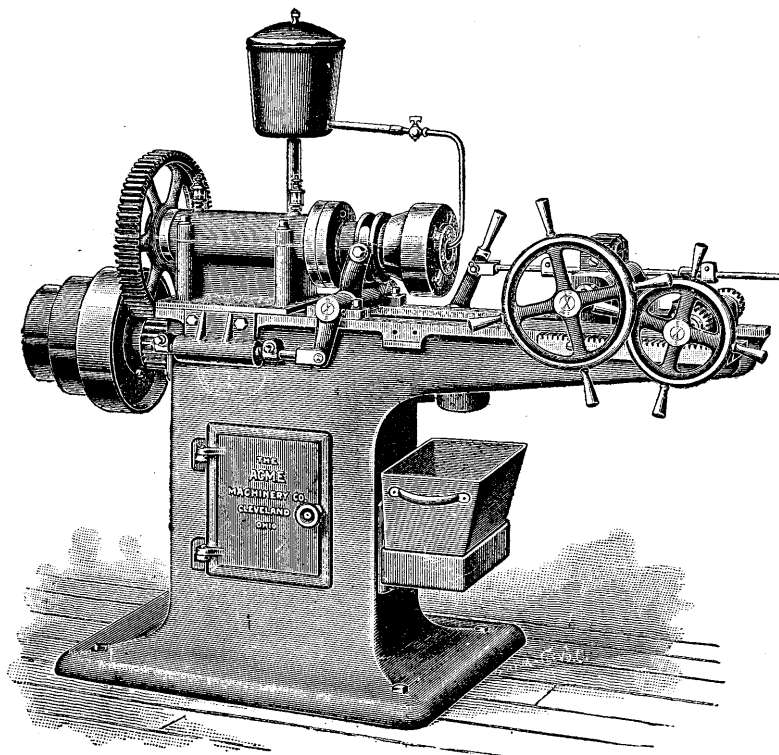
Taraudeuse de l'Acme Machinery Company, de Cleveland (E. U.).
